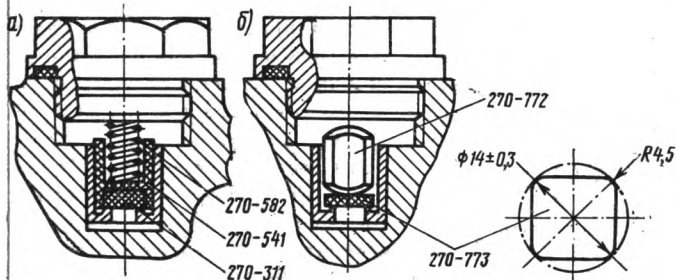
Обратный клапан главной части воздухораспределителя усл. № 270-005-1 и 270-002:
